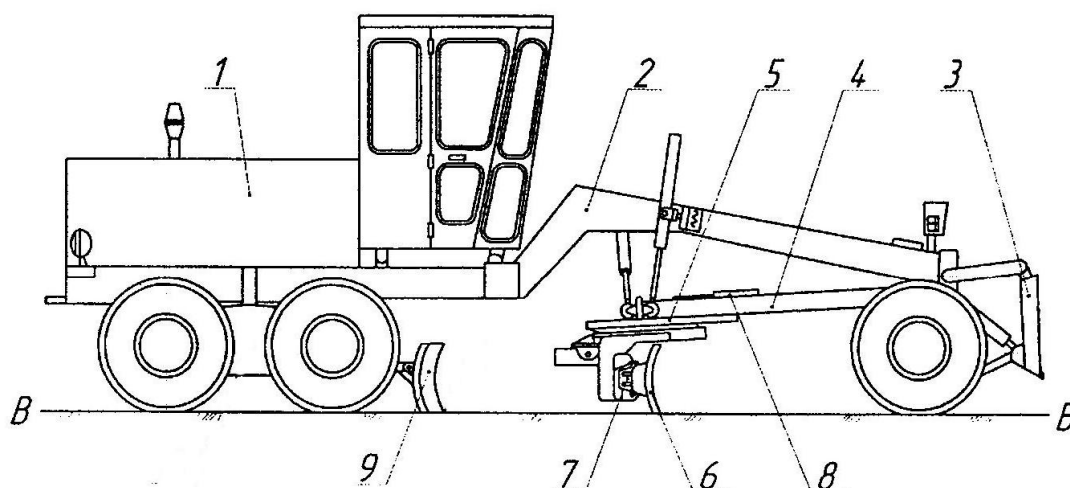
Общий вид автогрейдера с дополнительным бульдозерным оборудованием: 1 – силовая усновка; 2 – основная рама; 3 – бульдозерный отвал; 4 – тяговая рама; 5 – поворотный круг; 6 – планировочный отвал; 7 – гидроцилиндр бокового выдвижения отвала; 8 – привод поворота отвала; 9 – зачистный отвал;
